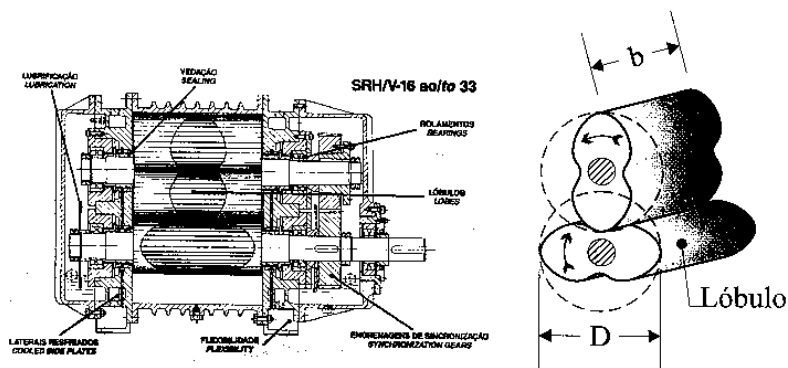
Compressor ou soprador de lóbulos (Fonte: Omel)
